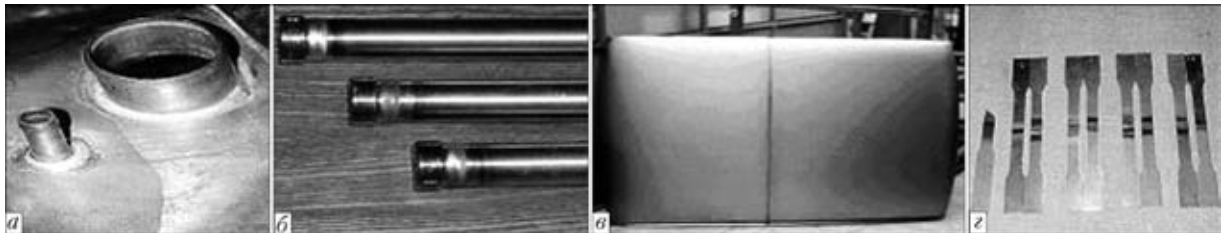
Примеры применения светолазерных технологий для сварки, наплавки и пайки: *а* — бензобаки автомобиля, изготовленные с применением световой технологии без нарушения антикоррозионного покрытия в зоне нагрева; *б* — корпуса источников ионизирующего излучения; *в* — детали кузова (крыши автомобилей); *г* — тестирование механических свойств сварных соединений
